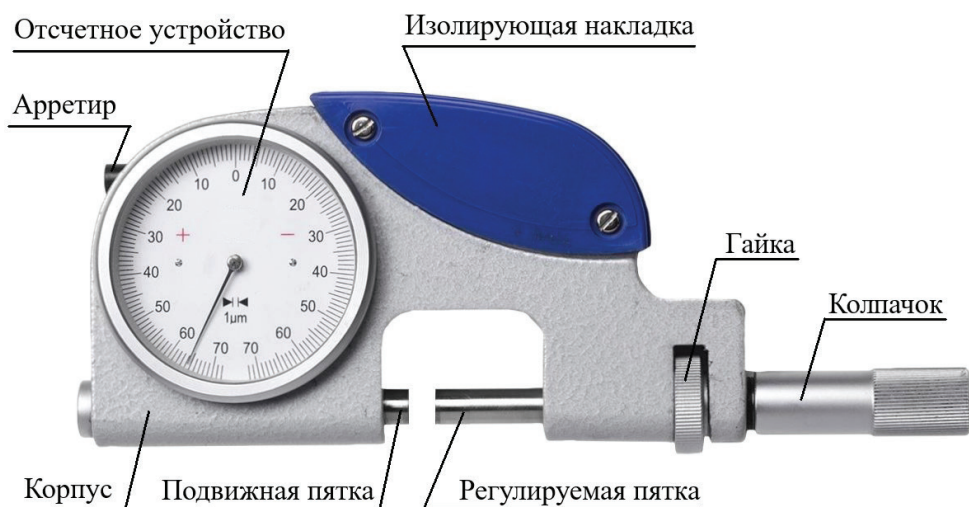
Основные элементы конструкции рычажной скобы [3]
